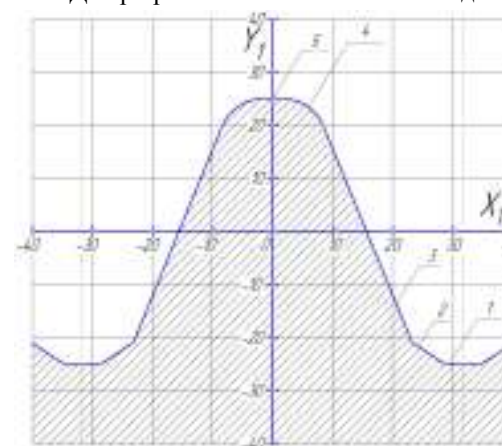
Теоретический профиль зуба исходного формообразующего реечного контура с модифицированным профилем у ножки зуба рейки (контршаблон исходного контура)
